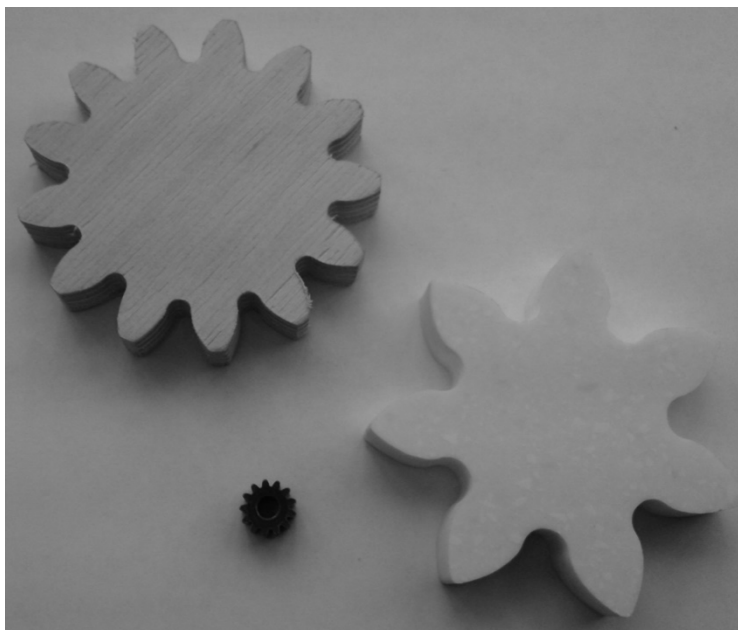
Эвольвентные зубчатые колеса, полученные контурным фрезерованием и электроэрозионным зубовырезанием
